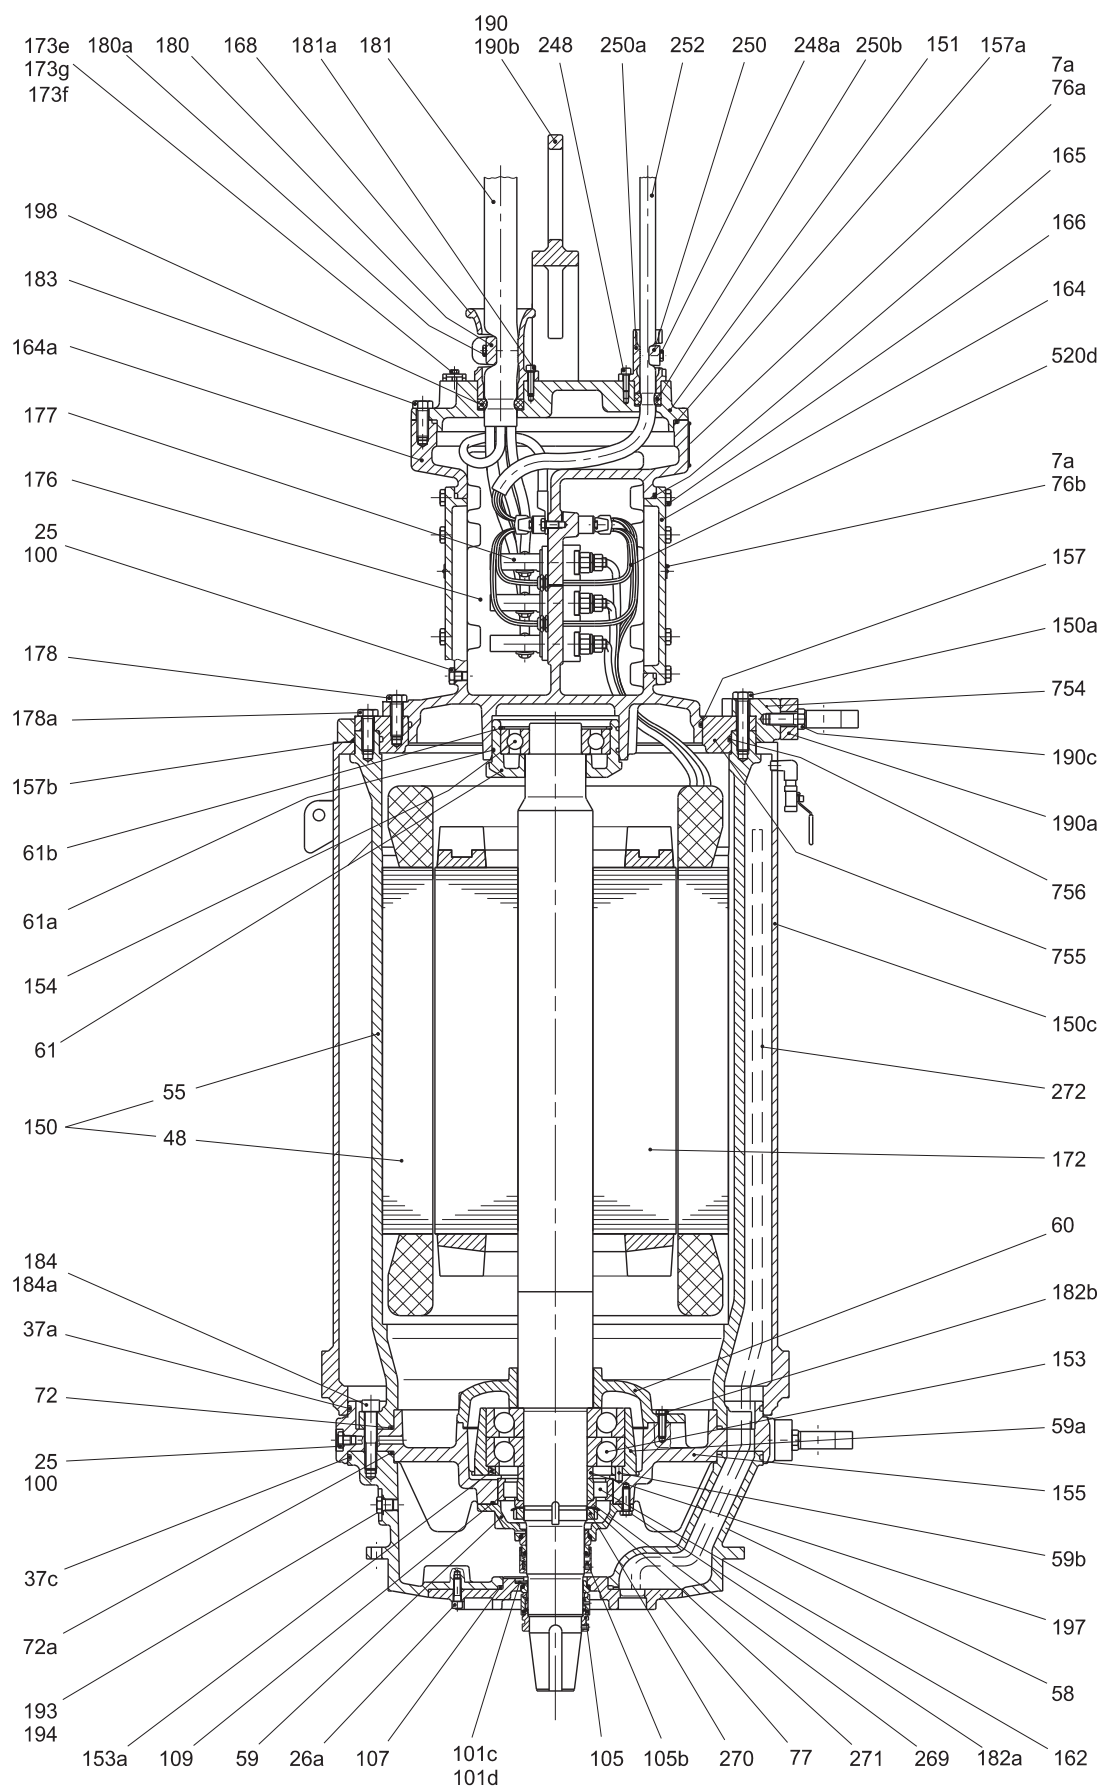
Типоразмер 74, невзрывозащищённый двигатель с охлаждающим кожухом.
